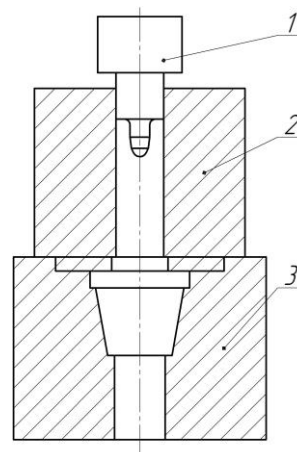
Пристосування для відновлення роздаванням хвостової частини корпусу різця дорожньої фрези: 1 – пуансон, 2 – направляюча, 3 – матриця
